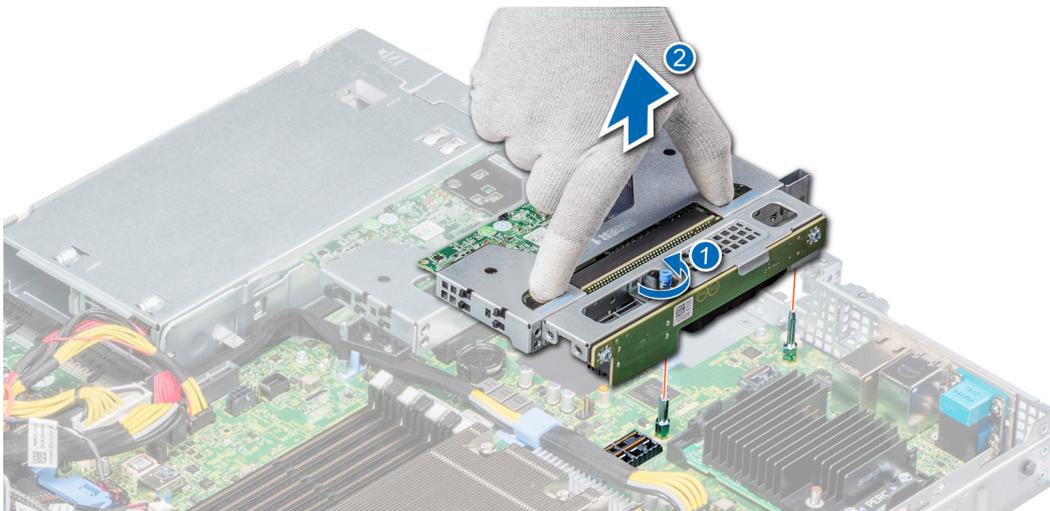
Extracción del soporte vertical de bajo perfil derecho
